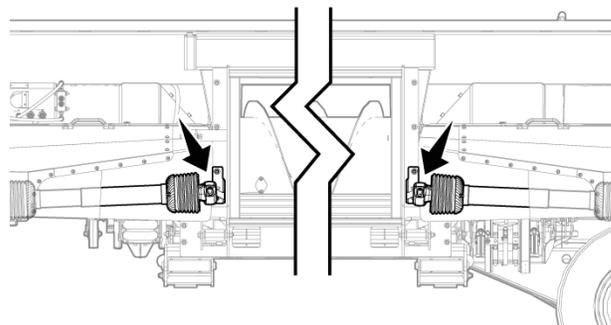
Posizioni di stoccaggio dell'albero motore
